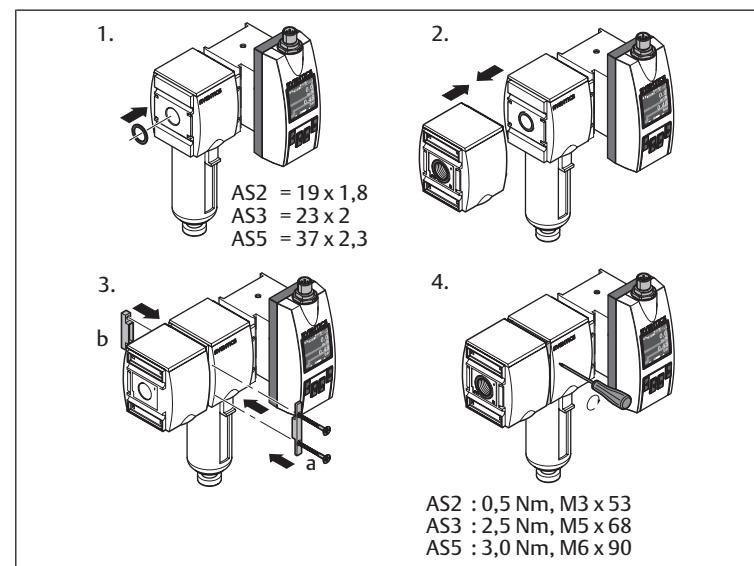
Montaggio con set per il montaggio in batteria | W04
